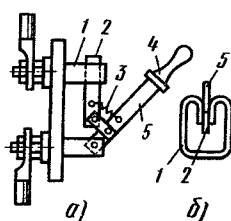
Рубильник с дугогасительным (моментным) ножом:
